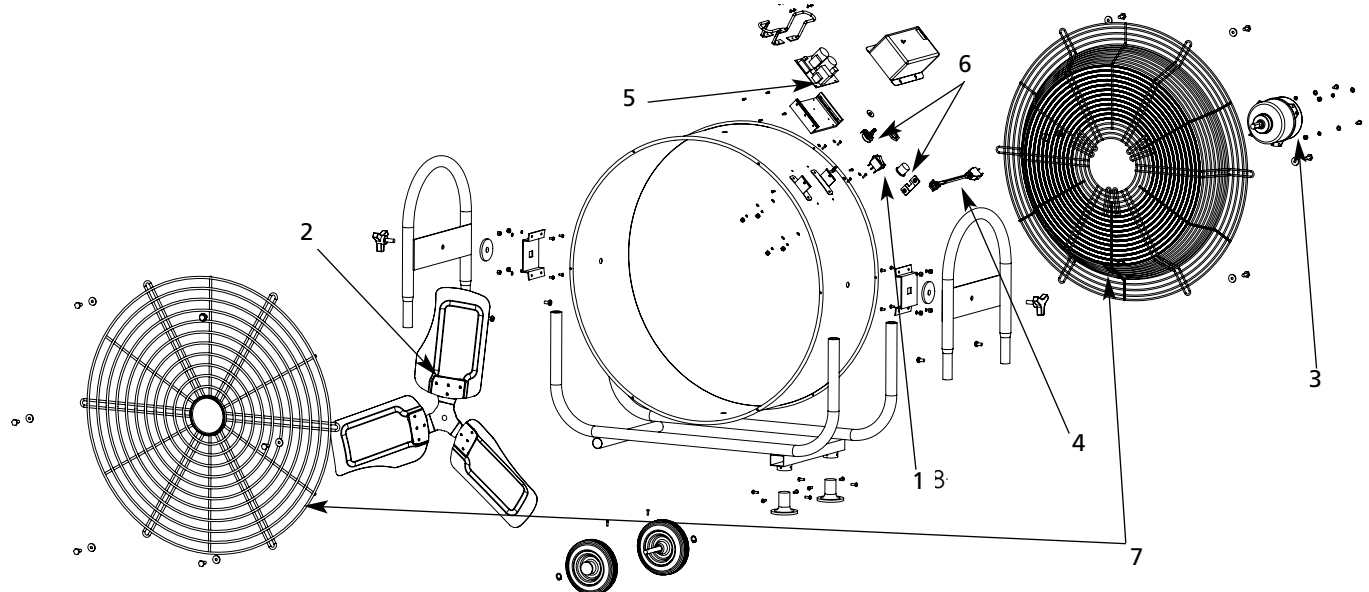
Illustration de Pièce de Réparation pour Circulateur de Air Mobile BLDC 31XL41
